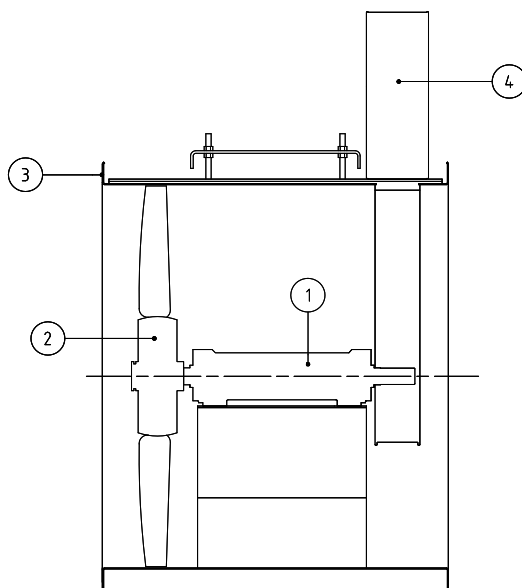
Assemblaggio di ventilatore assiale esecuzione 1
